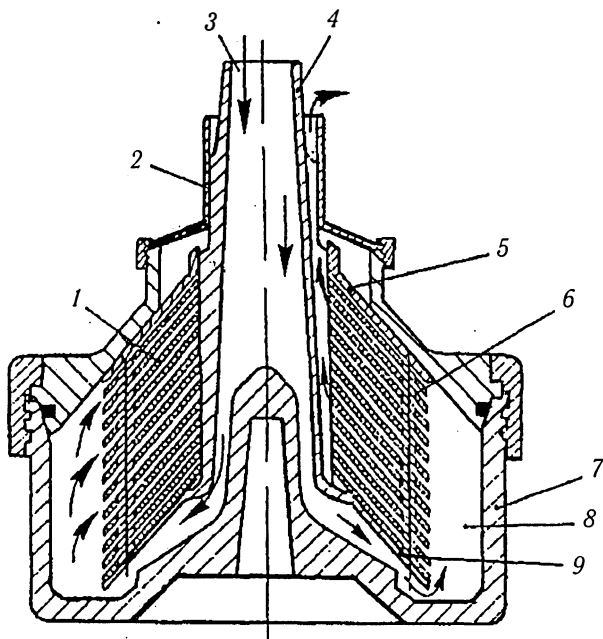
Схема барабана — кларификатора: 1 — пакет тарелок барабана; 2 — кларификаторная насадка; 3 — центральный канал; 4 — тарелкодержатель; 5 — верхняя защитная тарелка; 6 — каналы в тарелках (образованные отверстиями в тарелках); 7 — барабан; 8 — шламовая камера; 9 — нижняя сплошная тарелка
